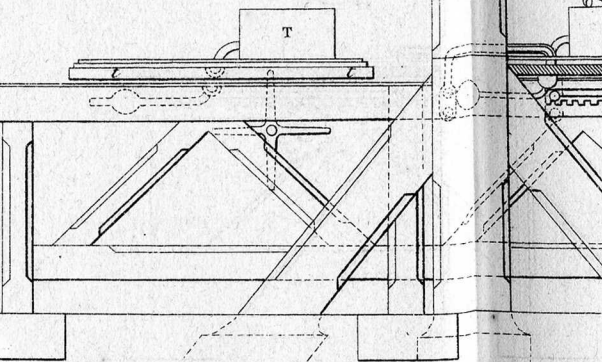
Vue de bout. A side view of the machine's frame and rollers.
